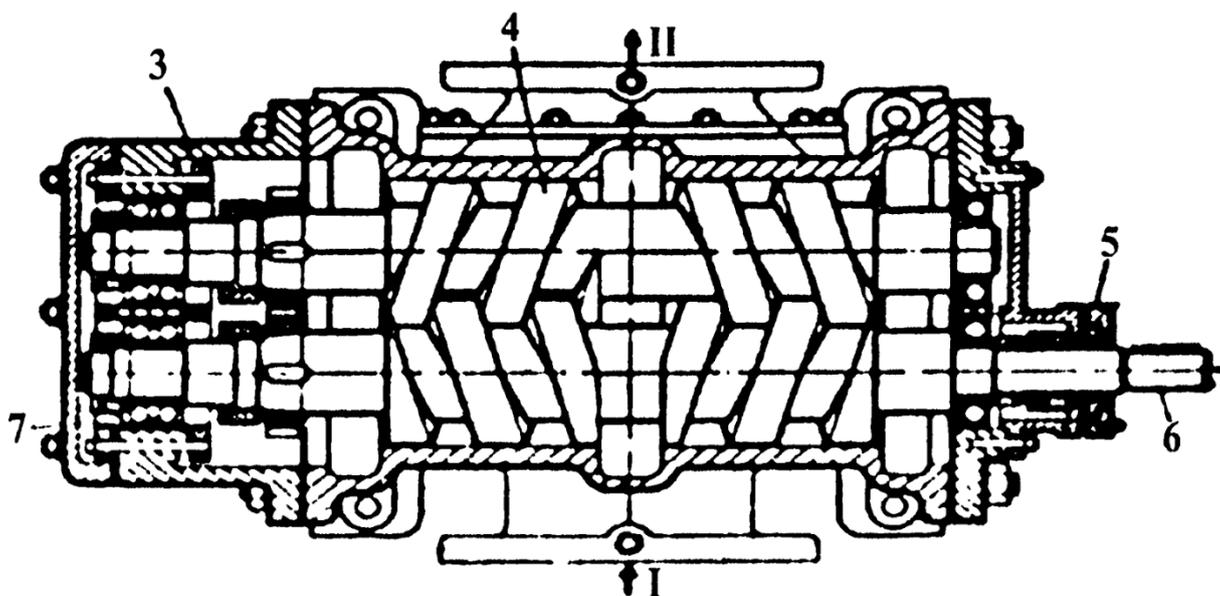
Винтовой насос. 3 — корпус; 4 — винт-ротор (ведомый); 5 — сальниковое устройство; 6 — винт-ротор (ведущий); 7 — подшипник качения; 1 — всасывающий патрубок; 2 — нагнетательный патрубок.
